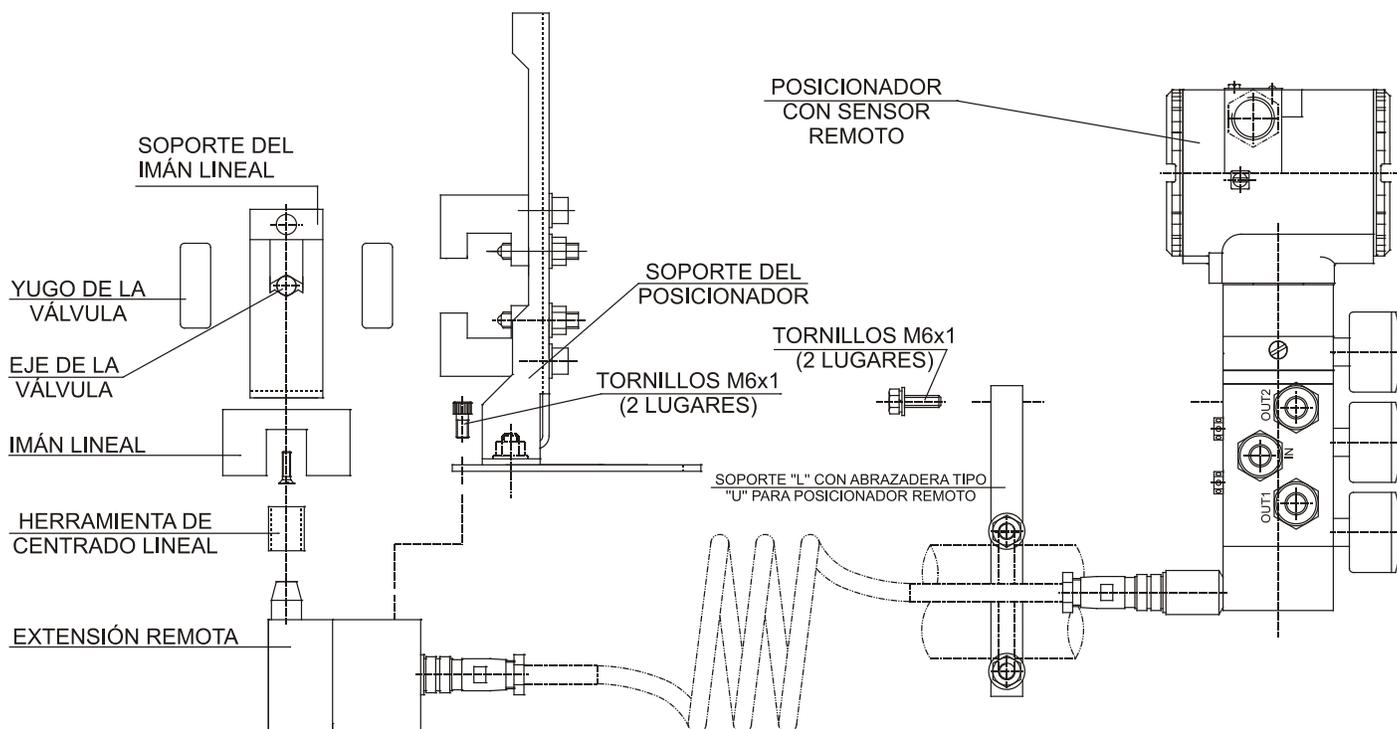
Posicionador en el Actuador Lineal con Posición Remota
